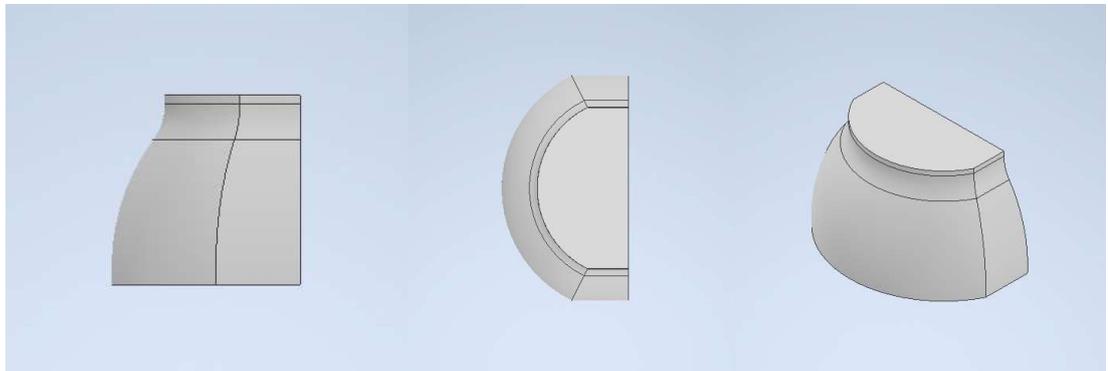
Perfil, planta y vista en perspectiva de la barriga.
